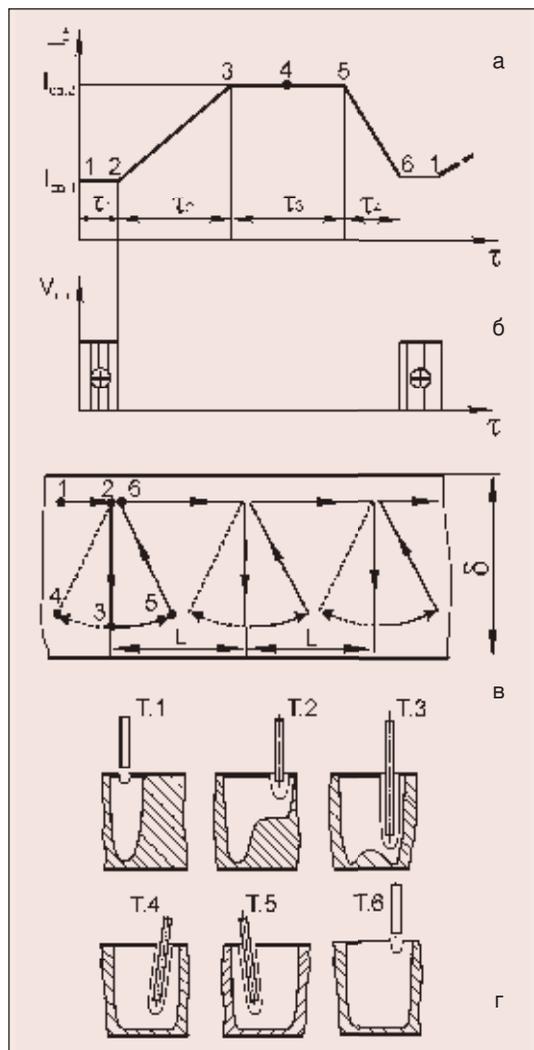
Способ сварки по схеме III: а — характер изменения силы сварочного тока; б — график перемещения сварочной головки; в — характер перемещения дуги в свариваемой плоскости; г — кинетика плавления основного металла
